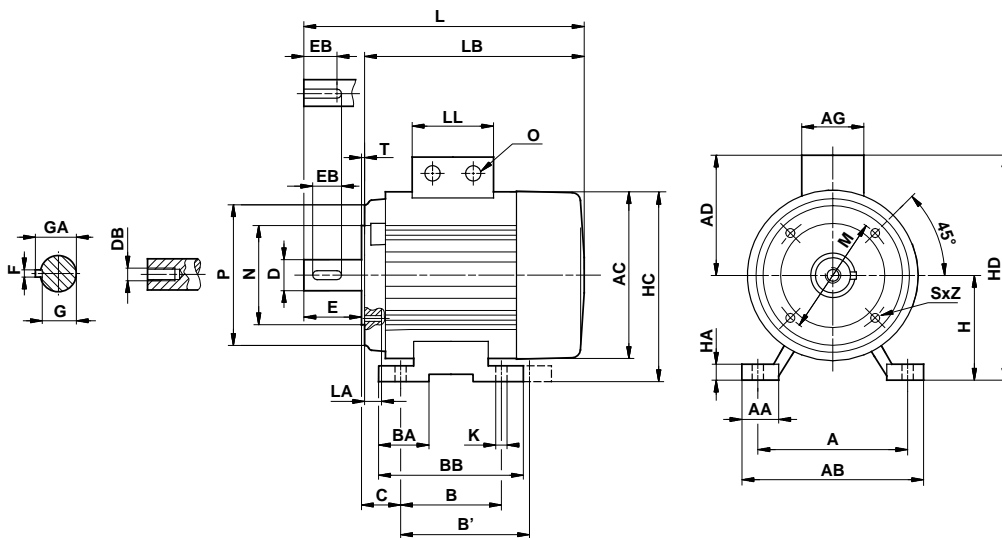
Foot-mounted motor with tapped-hole flange, IM B 34
